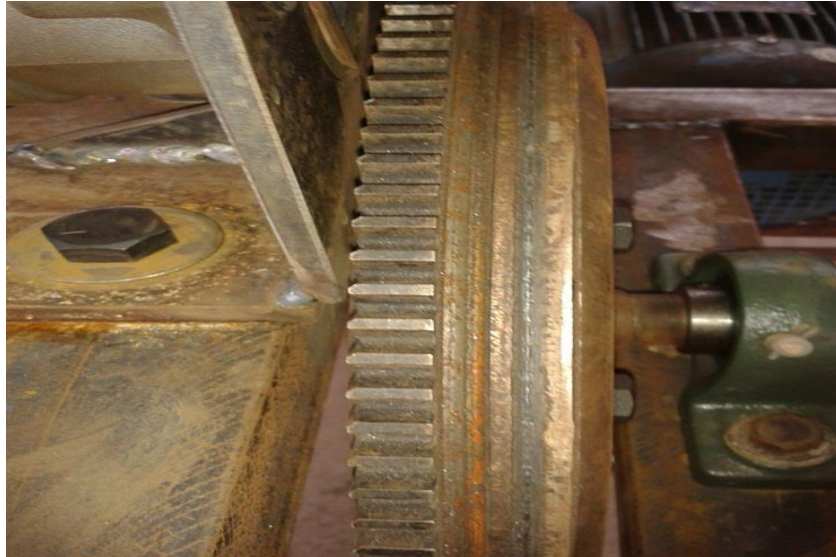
Montaje de elementos 2 en la estructura en el banco
